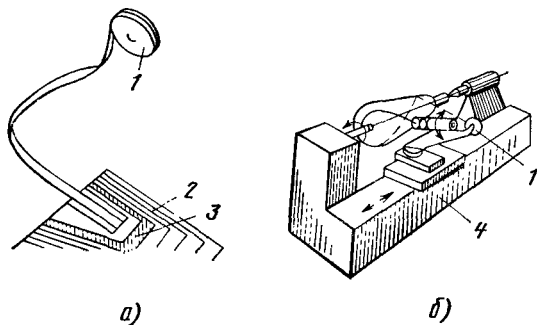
Схема оборудования для изготовления изделий из композиционных материалов методами: а — выкладки; б — намотки; 1 — катушка с лентой (препрег); 2 — установка для выкладки ленты; 3 — заготовка детали (изделия); 4 — намоточный станок с ЧПУ
